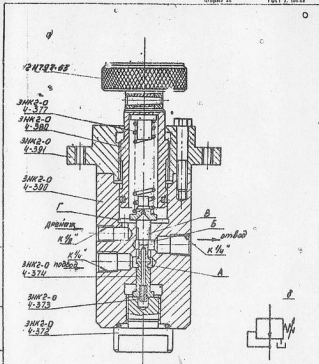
Клапан редукционный ЗНК2-0 С4-165
